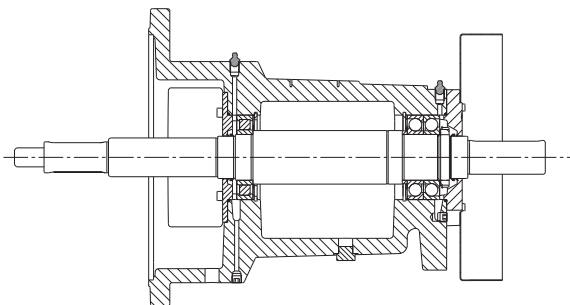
Корпус подшипников с закрытыми подшипниками с постоянной консистентной смазкой
